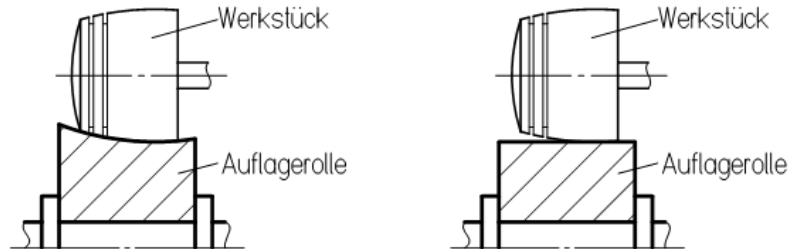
Formen der Auflagerrollen in axialer Richtung beim spitzenlosen Kolbenschleifen [ABL12a]
